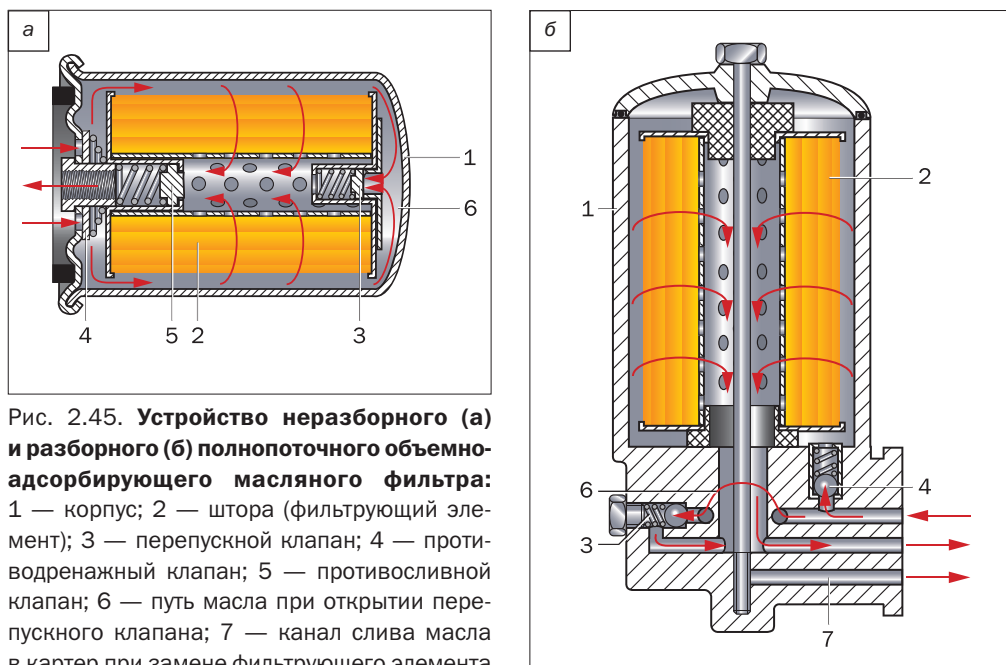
Устройство неразборного (а) и разборного (б) полнопоточного объемно-адсорбирующего масляного фильтра: 1 — корпус; 2 — штора (фильтрующий элемент); 3 — перепускной клапан; 4 — противодренажный клапан; 5 — противосливной клапан; 6 — путь масла при открытии перепускного клапана; 7 — канал слива масла в картер при замене фильтрующего элемента
